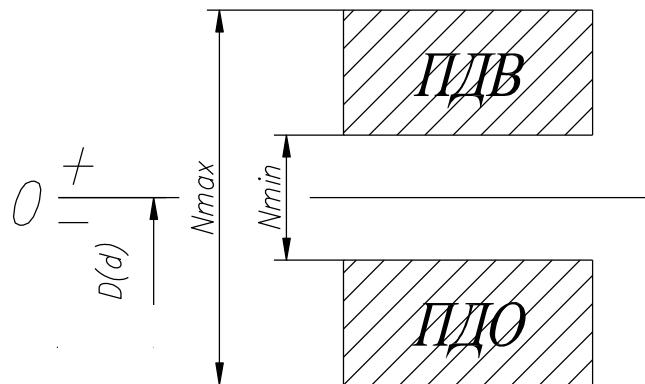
Схема розташування полів допусків з'єднання з натягом
